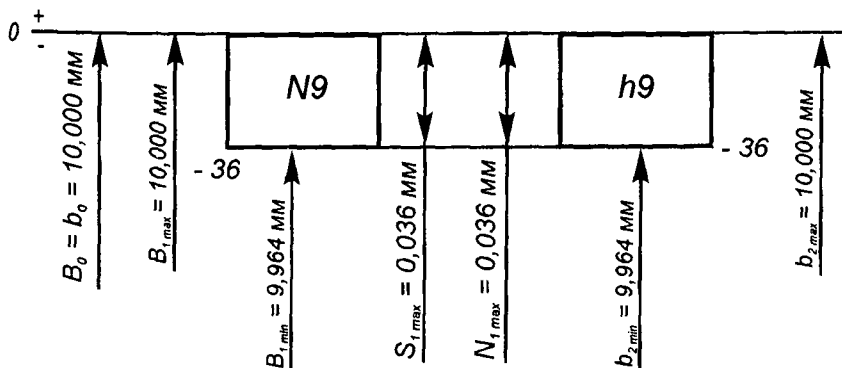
Схема расположения полей допусков ширины шпонки и ширины паза вала
